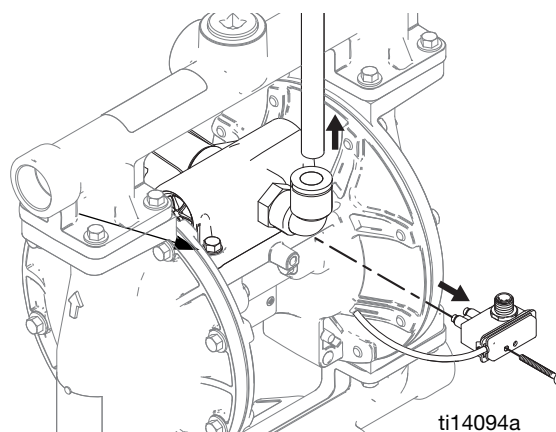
Conjunto del interruptor de lengüeta y extracción de la línea de aire
